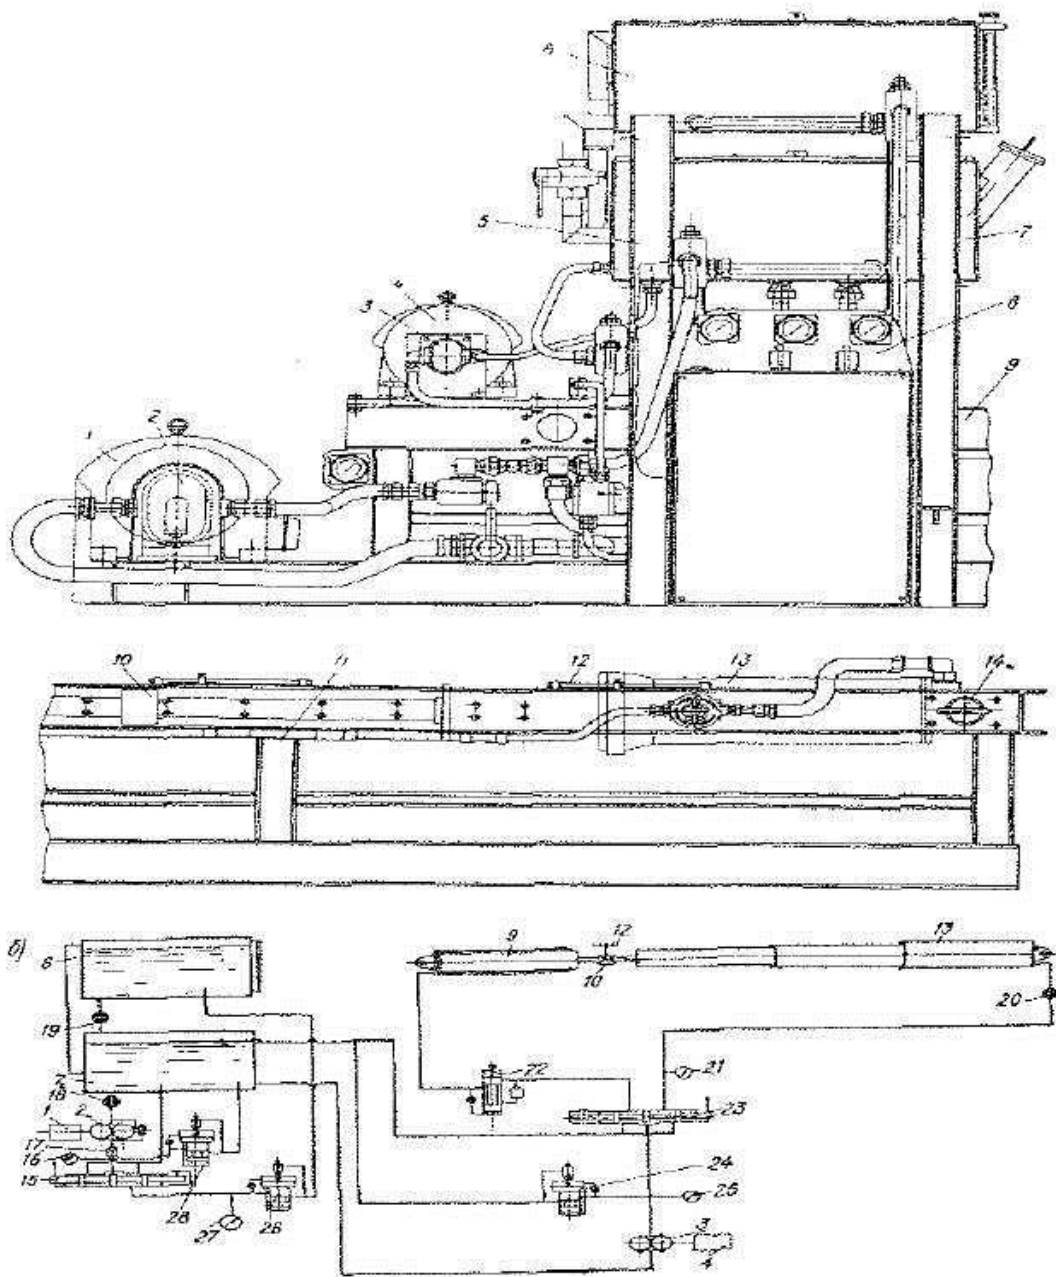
Стенд для испытания подъемного механизма автомобиля БелАЗ-525
